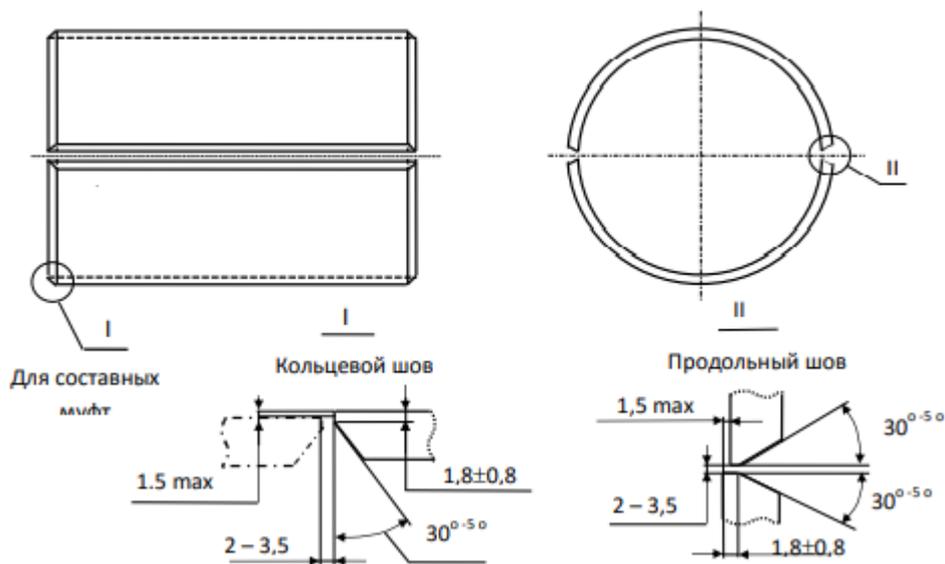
Разделка кромок полумуфт под сварку
